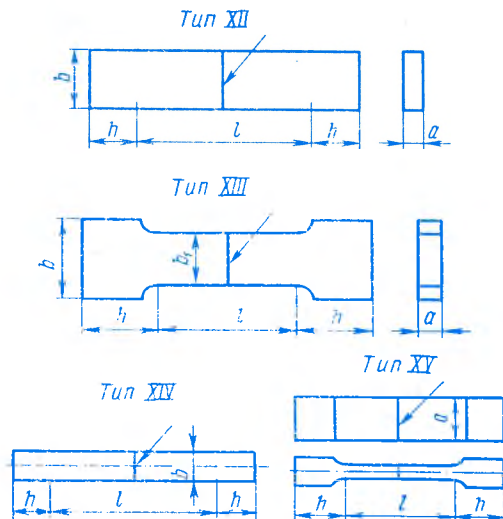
Различные типы образцов, предназначенных для испытаний сварных соединений на статическое растяжение:
